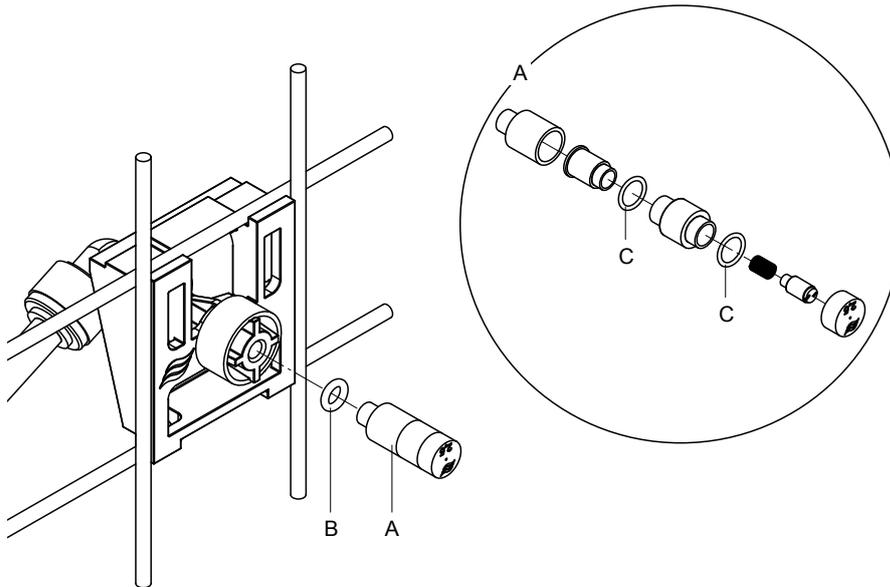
Montaje y desmontaje de las boquillas de pulverización
